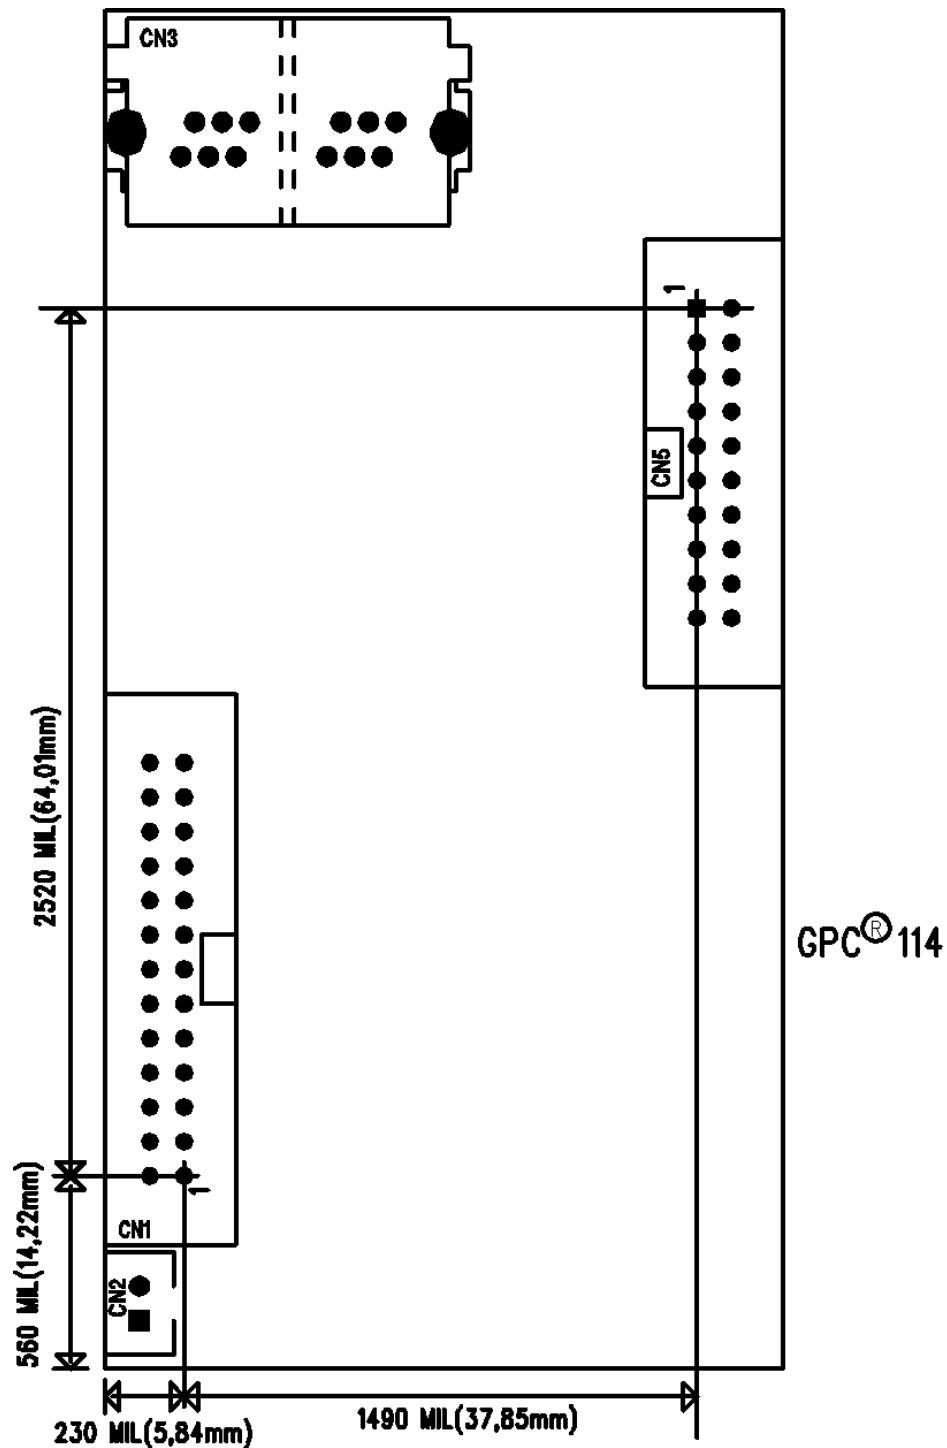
DIMA DI FORATURA PER MONTAGGIO IN PIGGY-BACK
